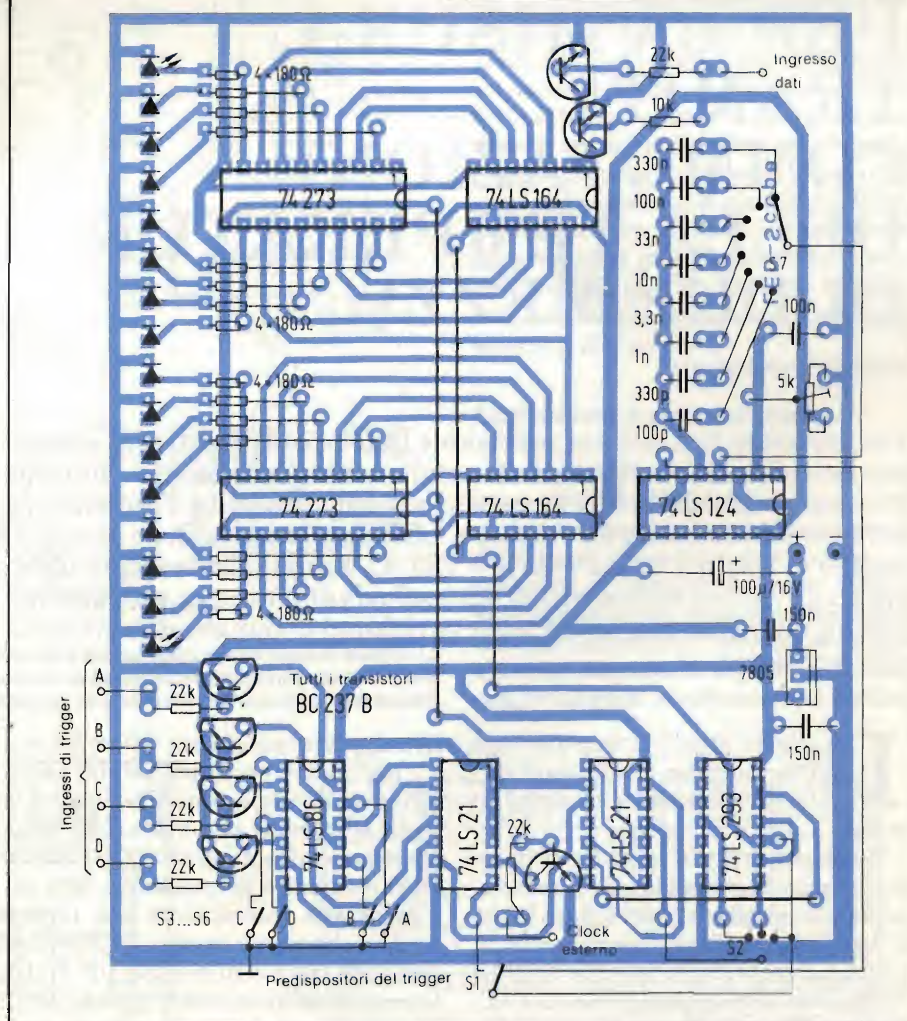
Disposizione dei componenti; osservando questo disegno sarà anche possibile effettuare il cablaggio esterno.
